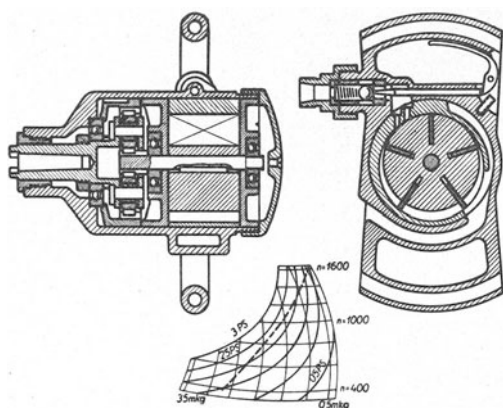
Böhler-Rotor-Kohlendrehbohrmaschine FK 64
